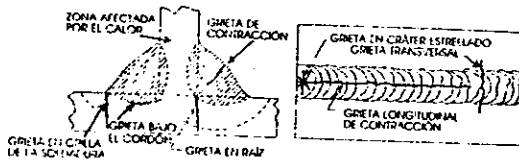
GRIETAS EN SOLDADURAS
